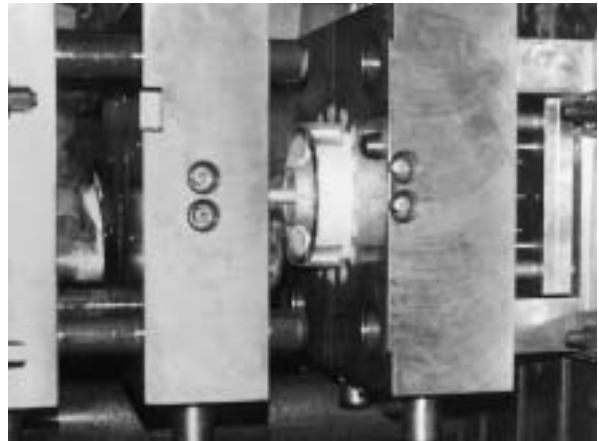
Dreiplattenwerkzeug auf einer Druckgießmaschine nach Öffnen der Form. Der Gießrest (links) ist vom Eingußzapfen abgerissen, und das Gußstück (rechts) ist frei zum Auswerfen. (Bühler Druckguss AG, Uzwil, Schweiz)
